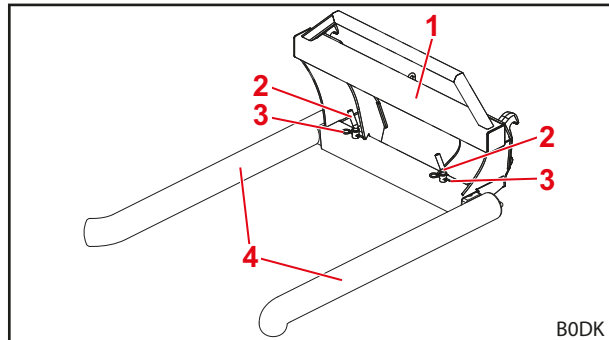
Конструкция вилок для перевозки тюков H – вид спереди
